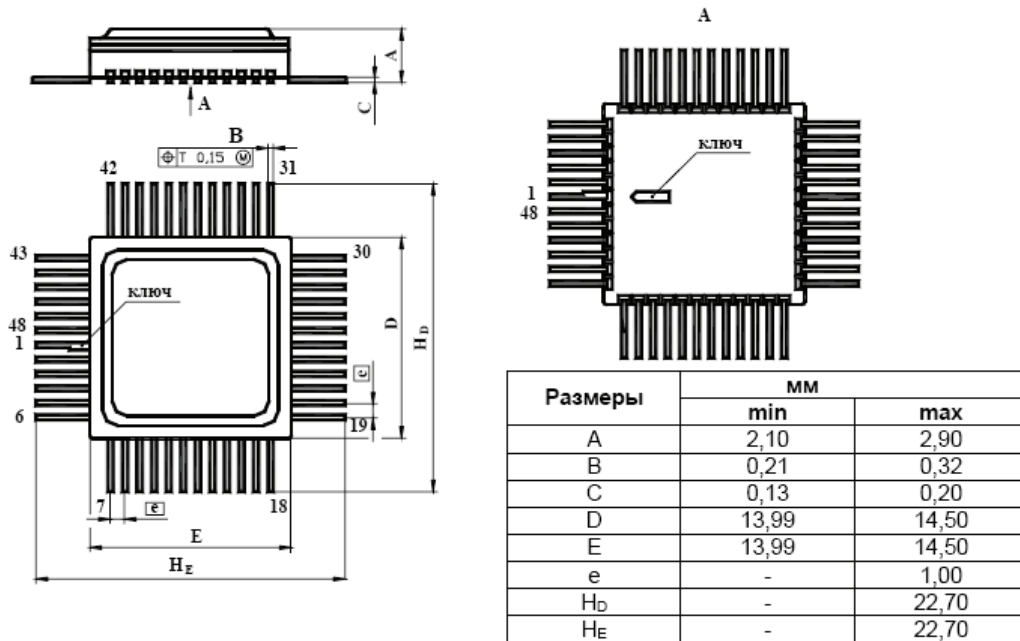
Габаритный чертеж корпуса H16.48-1B
